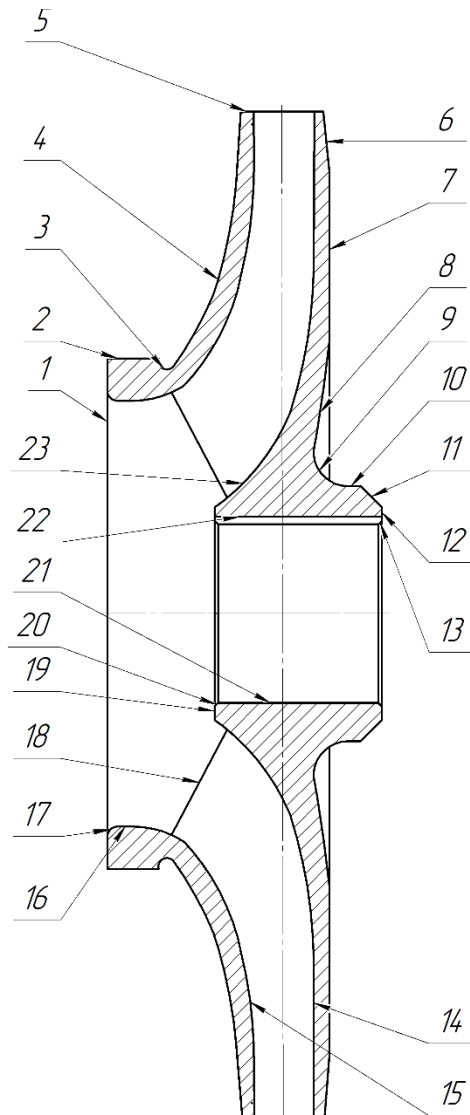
Ескіз класифікації поверхонь робочого колеса
